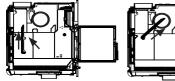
Pose de la pierre latérale arrière haut (H4-21) sur la pierre latérale bas droite et déplacement vers l'arrière jusqu'à la butée.
